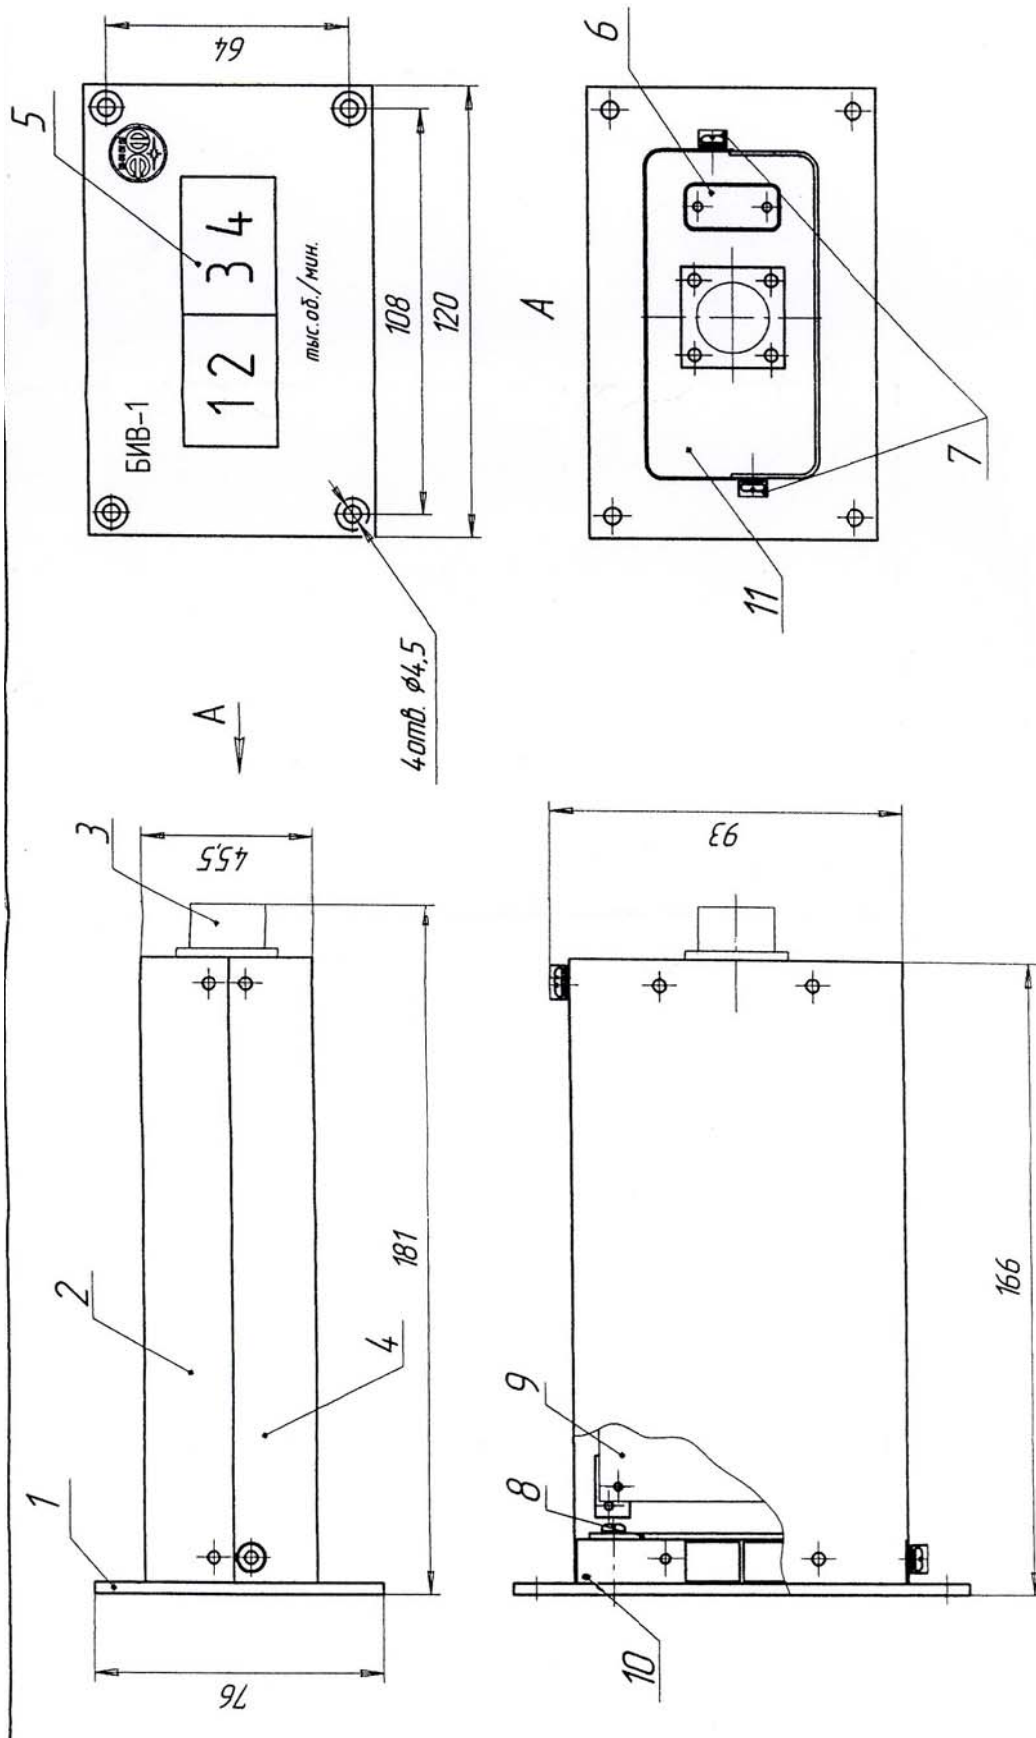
Внешний вид гибридные и присоединительные размеры МТ
